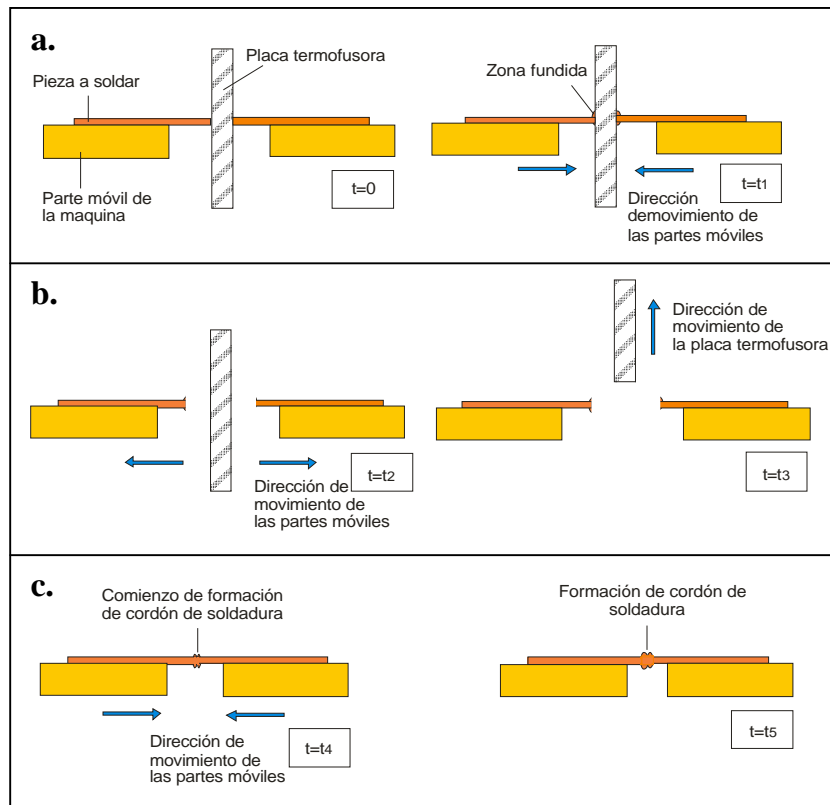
Proceso de soldadura por termofusión a tope.
